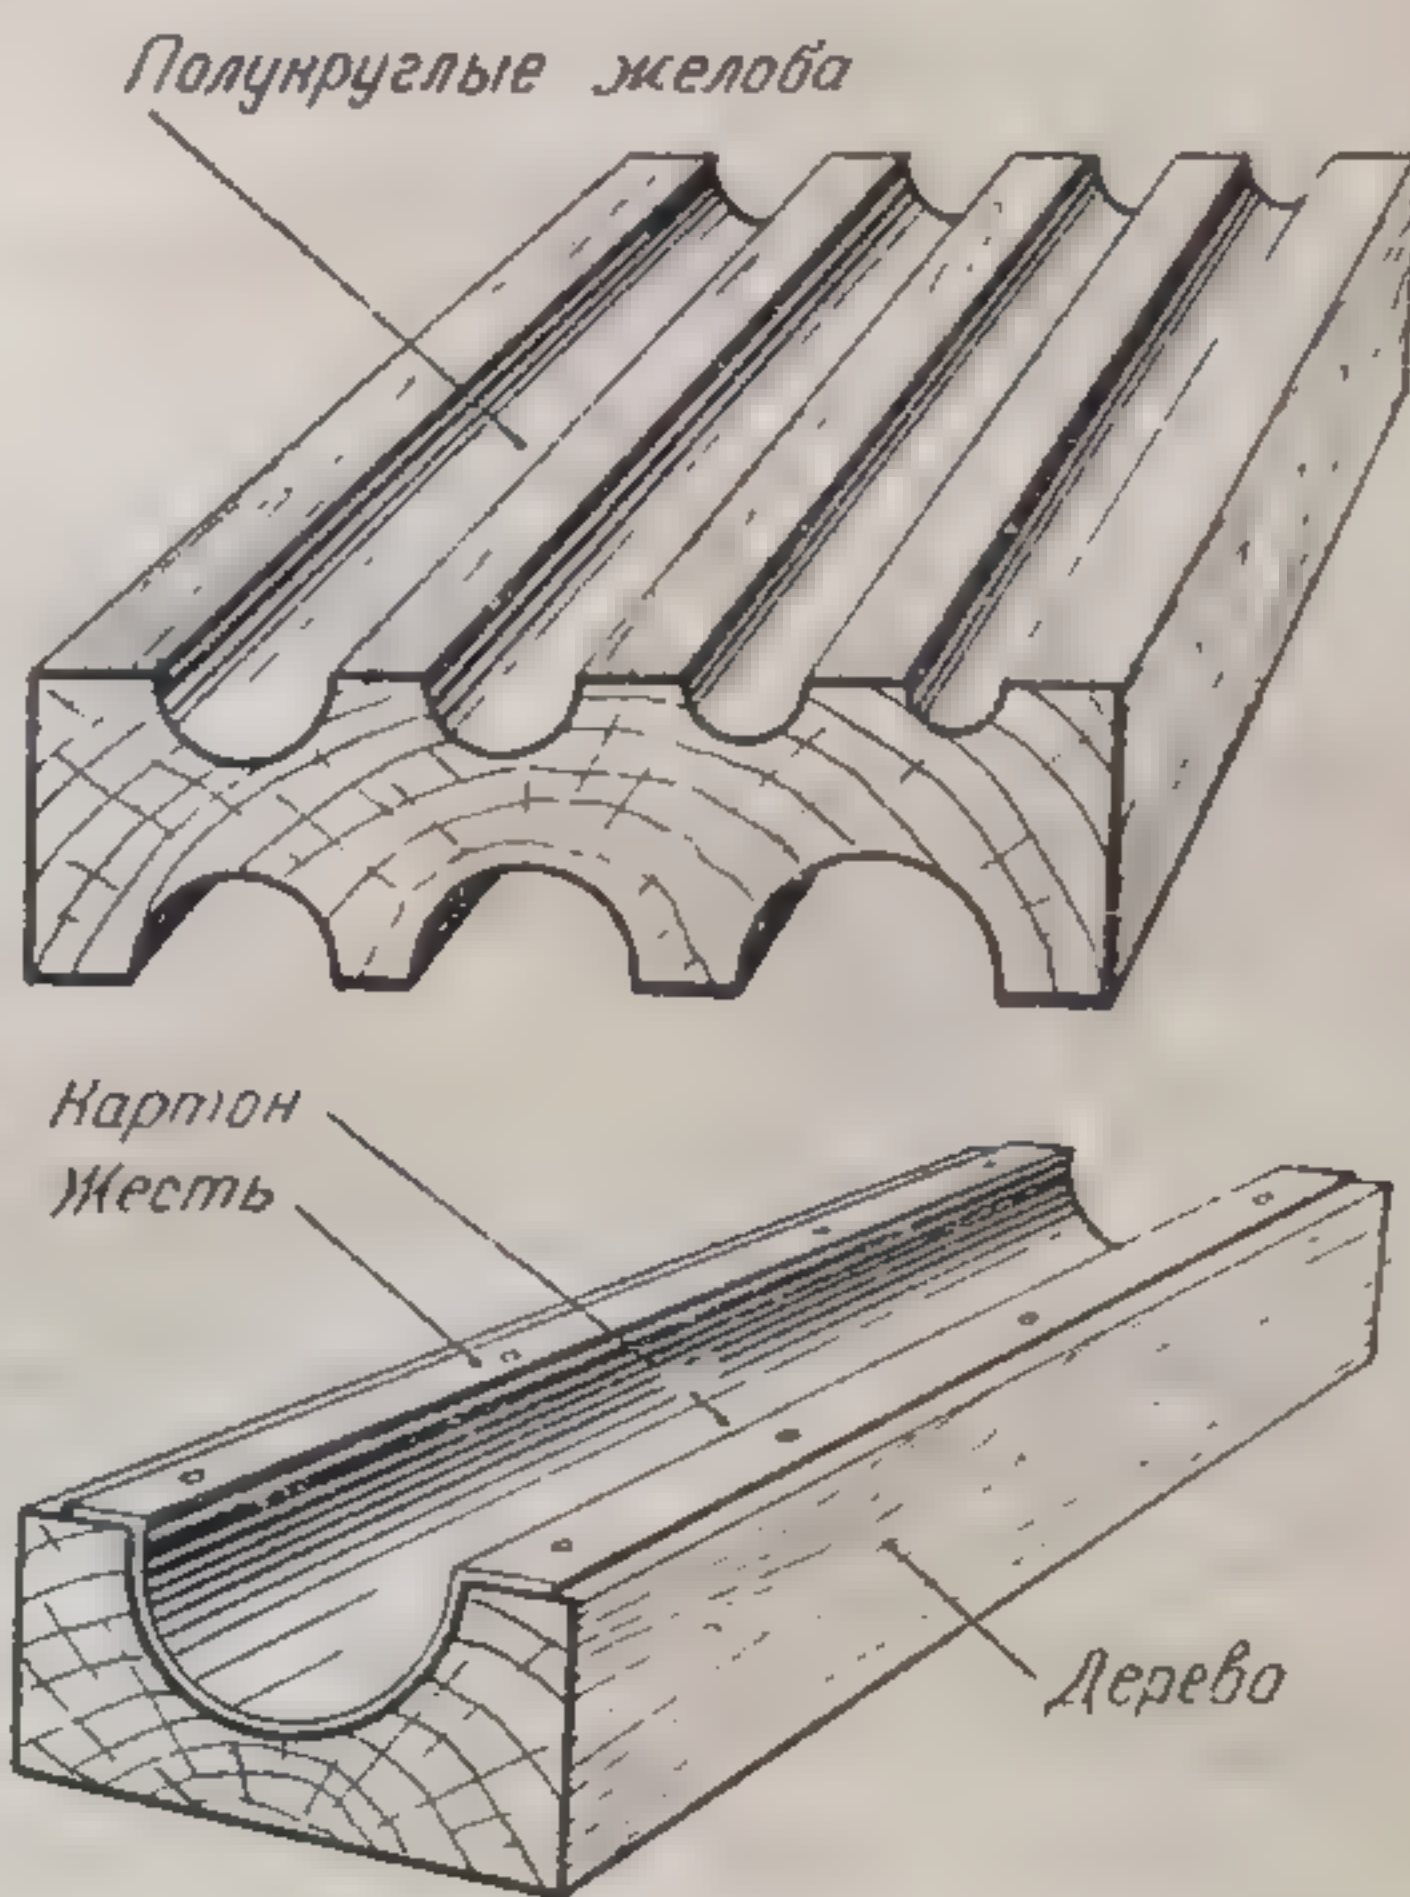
Приспособления для кругления корешка при бесшвейном скреплении блока
